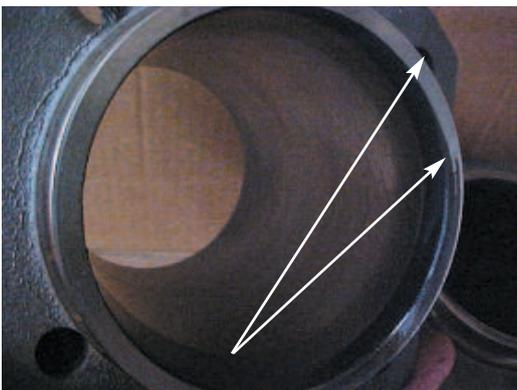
Apoyo irregular entre la parte superior de la camisa y la tapa de cilindro
